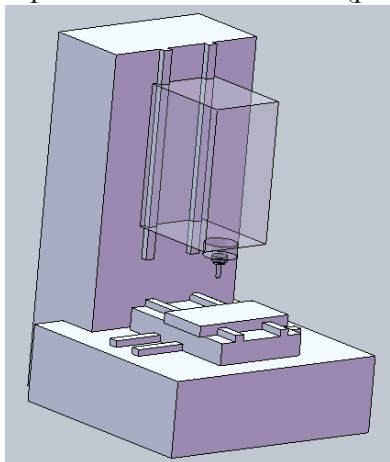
Компоновка обрабатывающего центра вертикально-фрезерного типа
